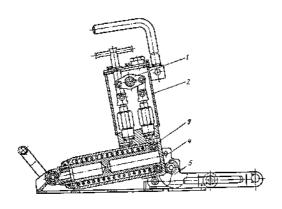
Гидравлический рихтовщик ГР-12Б [7] 1 — двух-плунжерный насос; 2 — резервуар с маслом; 3 — шток; 4 — трёхступенчатый рельсовый захват; 5 — опорное устройство
